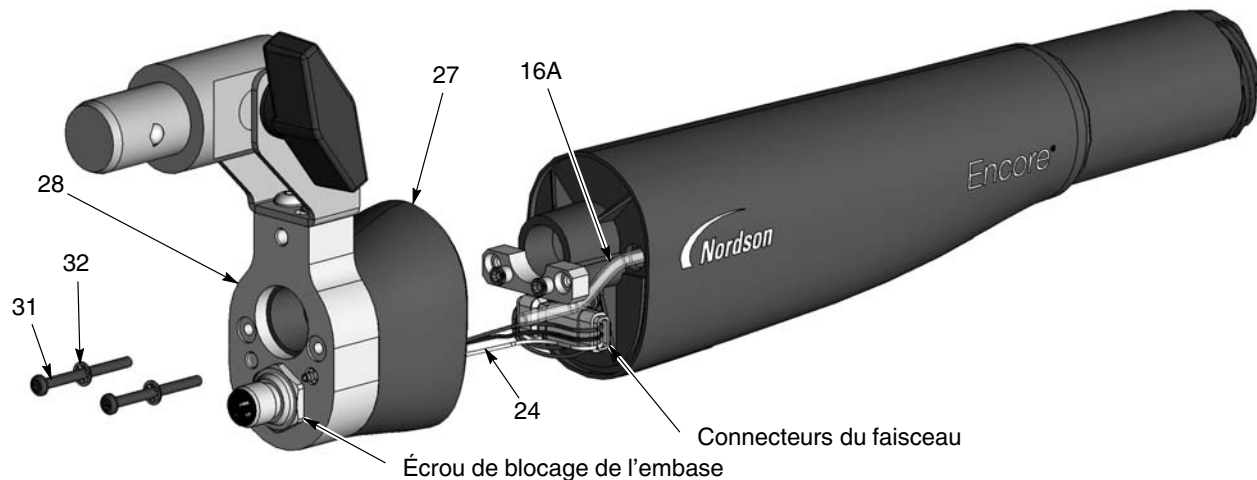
Démontage du pistolet – Remplacement du tube à poudre
